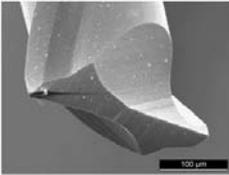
Schliessung der Fertigungskette mit eigener Beschichtung im Maschinenbau
